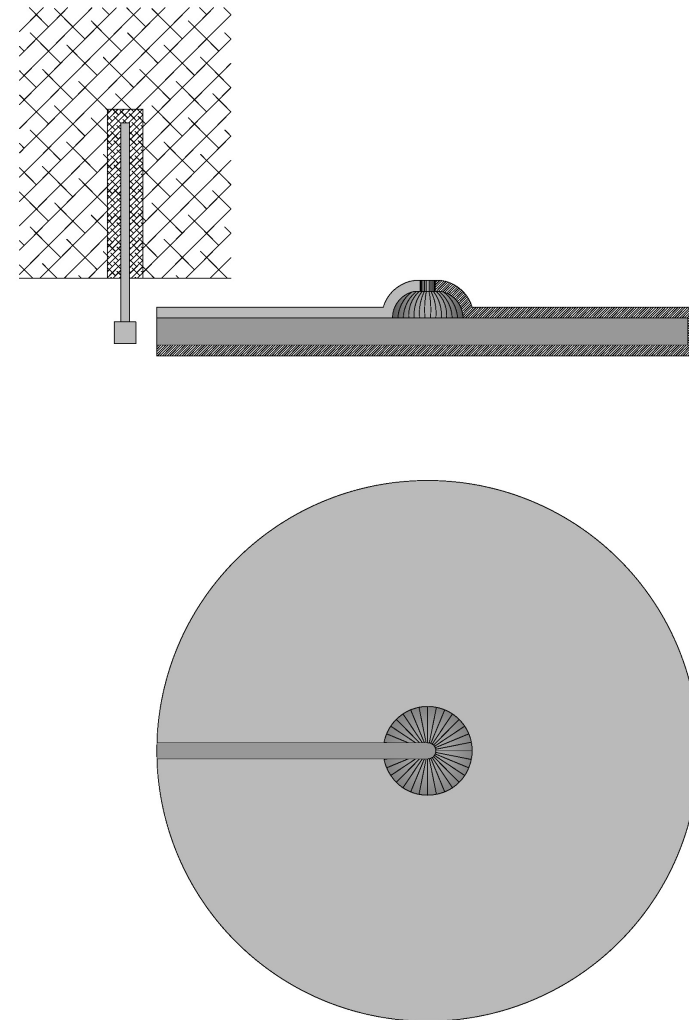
79 – Vulcanizzazione nell'isolatore di un cavetto in acciaio con un cilindro di fermo atto ad ancorare l'isolatore alla piastra d'acciaio in inox.
